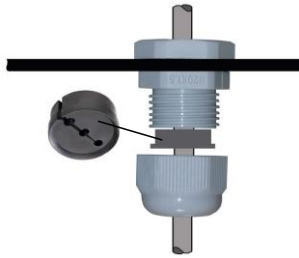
Kabeldurchführung mit geteiltem Dichtungseinsatz
